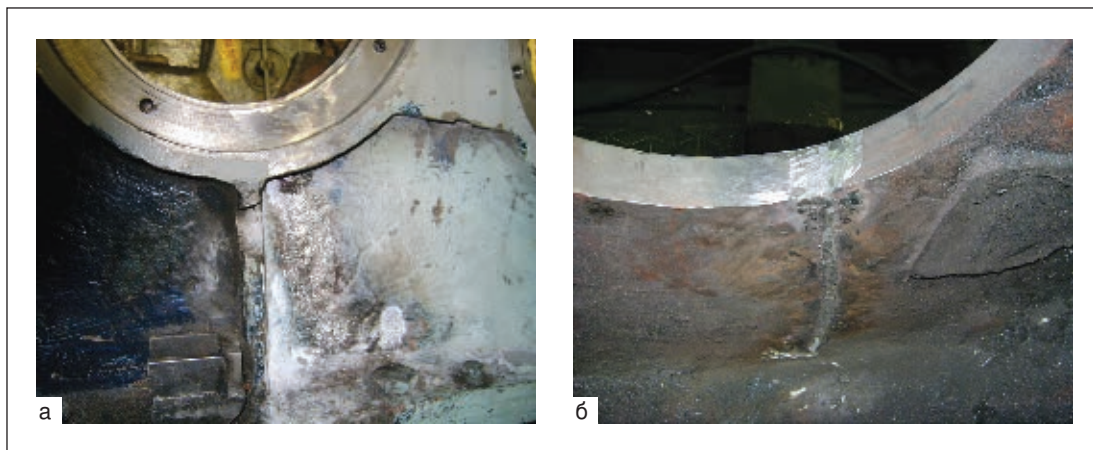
Восстановленное посадочное место подшипника в корпусе редуктора: а — основание; б — крышка
